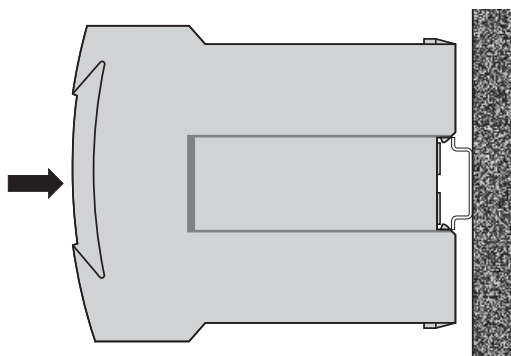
Montage sur rail «à chapeau» 35 × 15 ou 35 × 7,5 mm.
